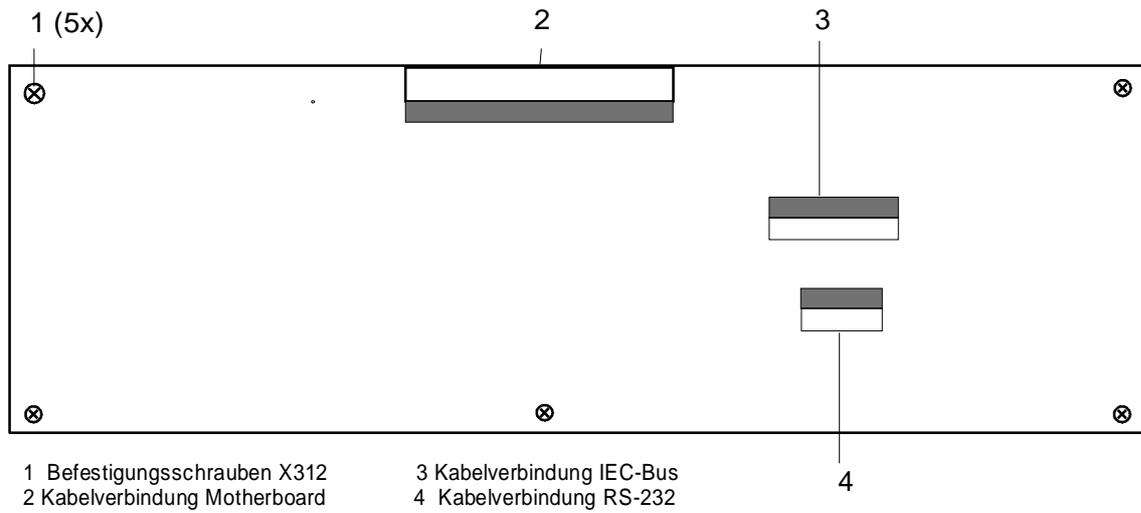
Abschirmdeckel von Steuerrechner und Frontplattenmodul
